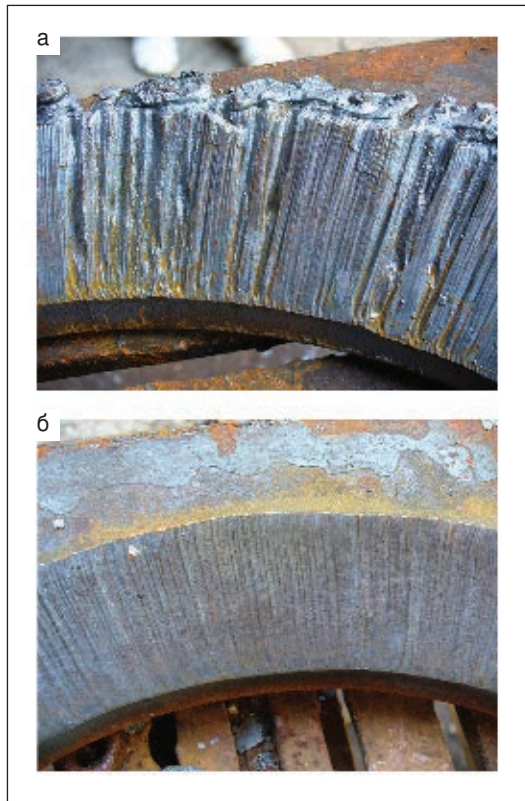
Качество реза фасок: а — ручным резакком; б — с использованием приспособления. Заготовки перевернуты
